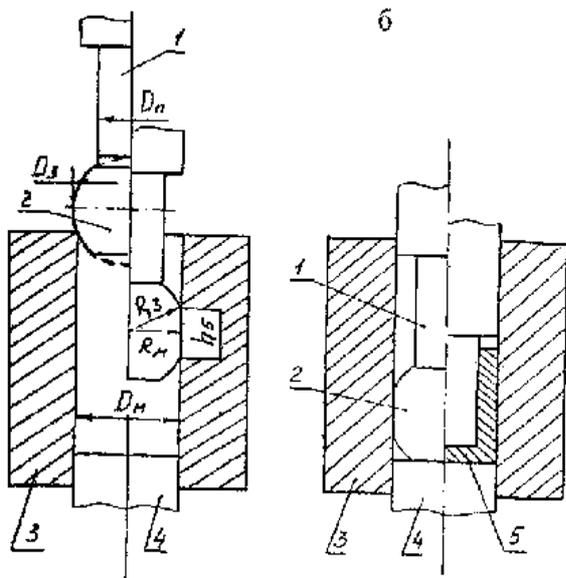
Исходное положение пуансона, заготовки и момент продвижения заготовки в матрице (а); процесс формирования полости и внешнего контура детали (б)
